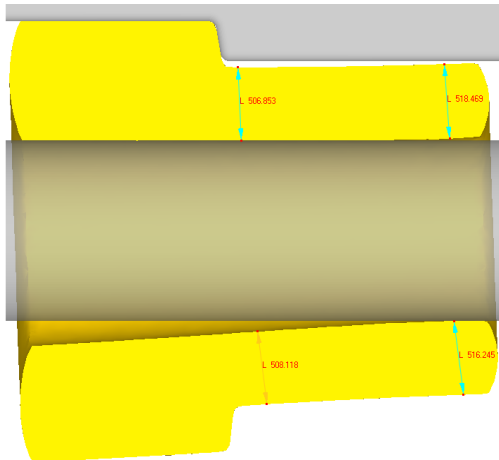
Змінення товщини стінки заготовки на початковому етапі розкочування
